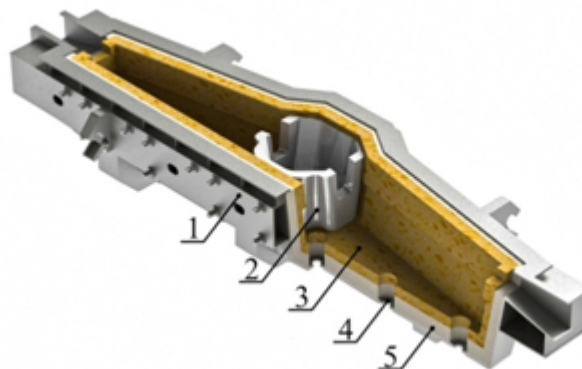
загальний вигляд 6-ти струмкового промковша сортового МБЛЗ: 1 - кожух промковша; 2 – металоприймач; 3 - робочий шар; 4 - склянка-дозатор; 5 - арматурний шар
